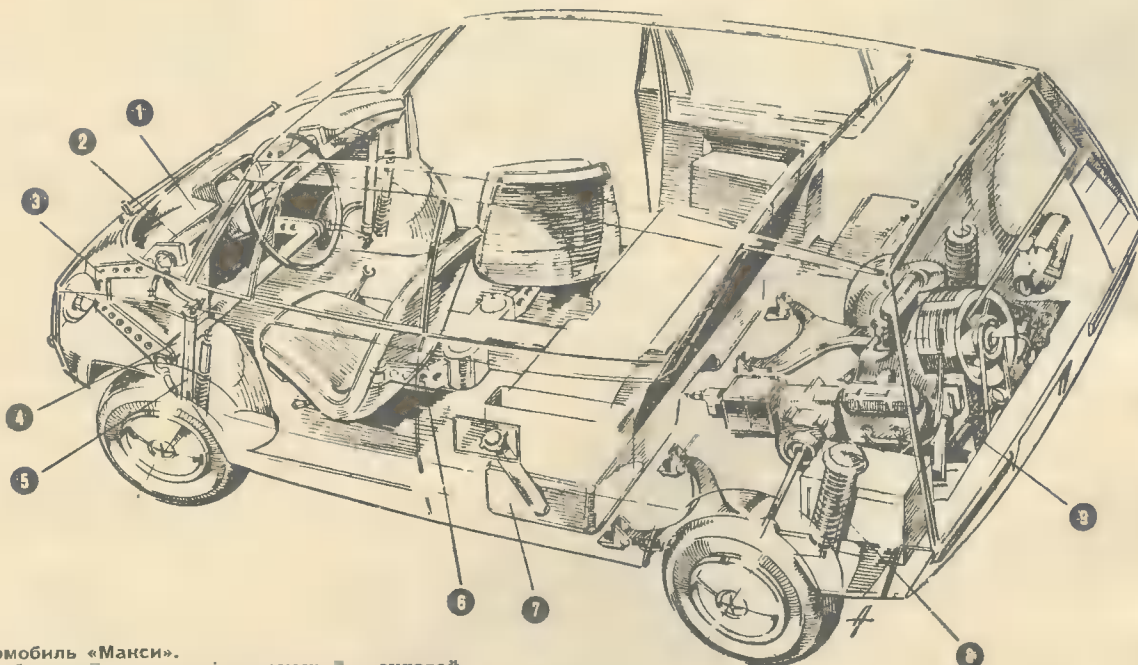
Автомобиль «Макси». 1 — щиток приборов; 2 — верхний торсион; 3 — силовой профиль; 4 — нижний торсион; 5 — поворотная стойка рычага передней подвески; 6 — поворотный кривошип; 7 — бензобак; 8 — задняя подвеска; 9 — двигатель.
